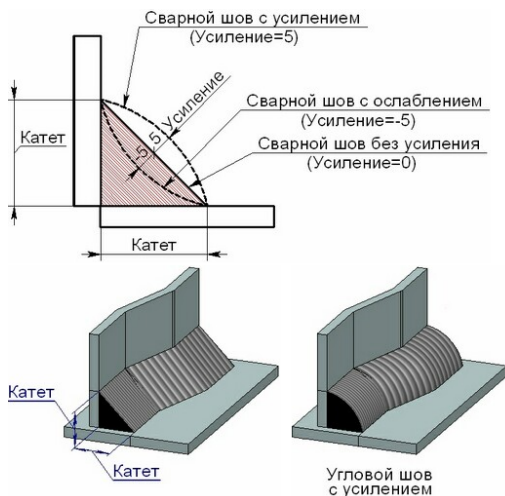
Значения катетов, ослабление/усиления создаваемого углового сварного шва
